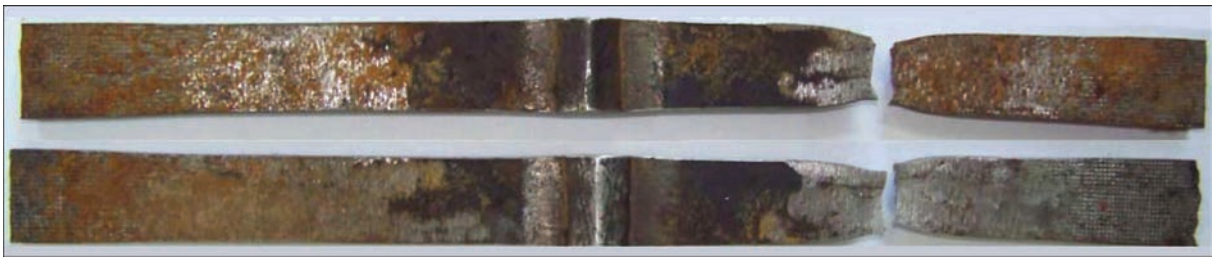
Внешний вид образцов сварного соединения после испытаний на статическое растяжение
